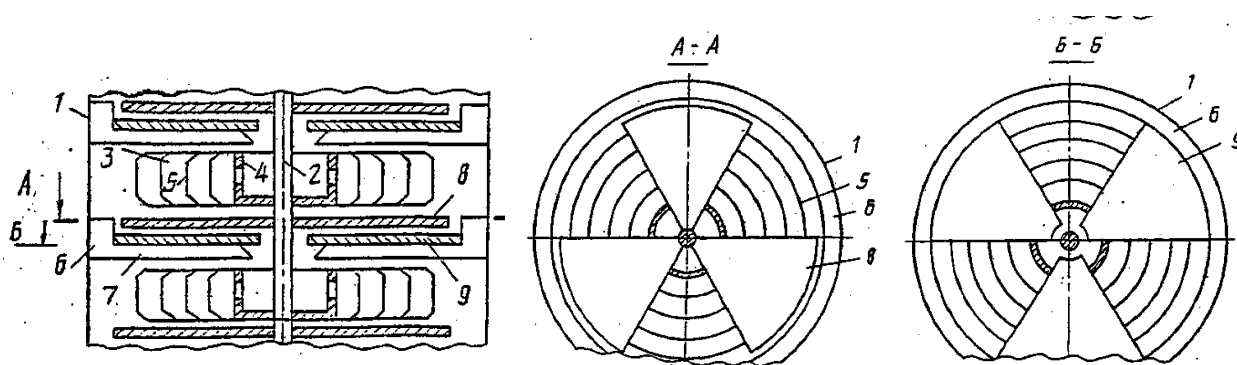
Роторная массообменная колонна: 1 – корпус; 2 – вал; 3 – контактная ступень; 4 – распределительный стакан; 5 – отбортованные цилиндры; 6 – кольцевой карман; 7 – сливные патрубки; 8 – лопасти; 9 – прорези.
